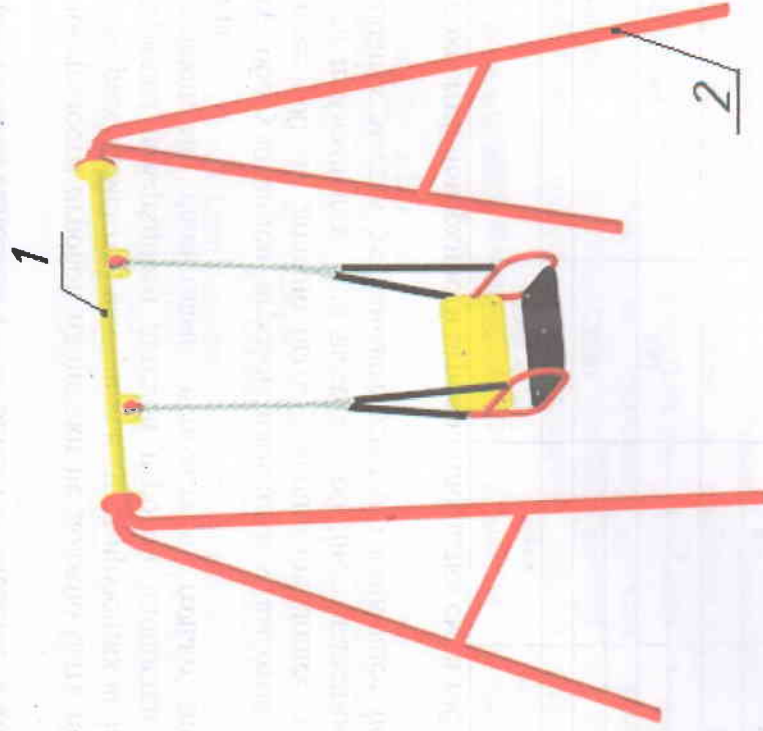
общий вид и схема сборки качелей с подвесом артикул П-05.
